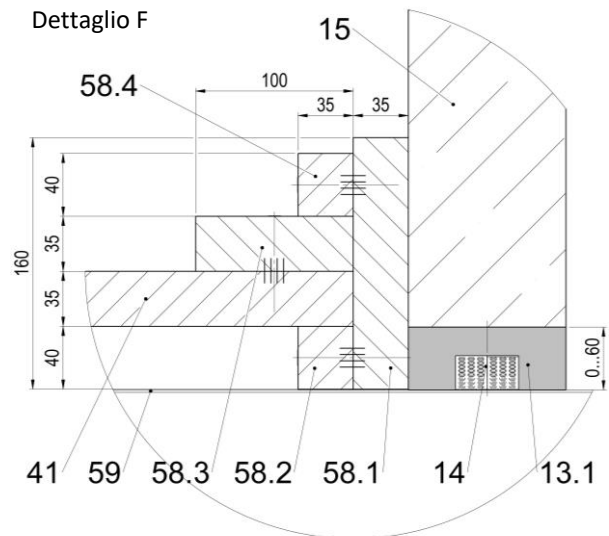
vista laterale (sezione) BKA-EN con controltaio tipo ERA2 montato
